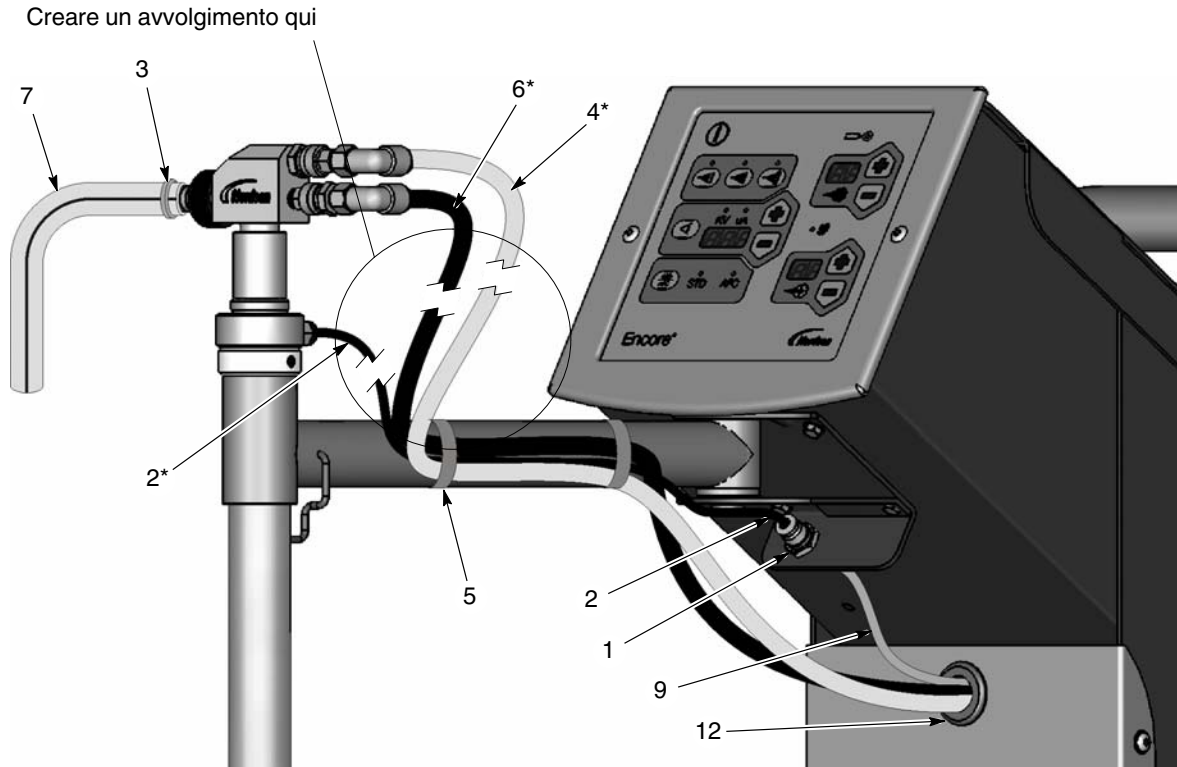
Installazione del tubo di raccolta e della pompa della pistola Encore LT
